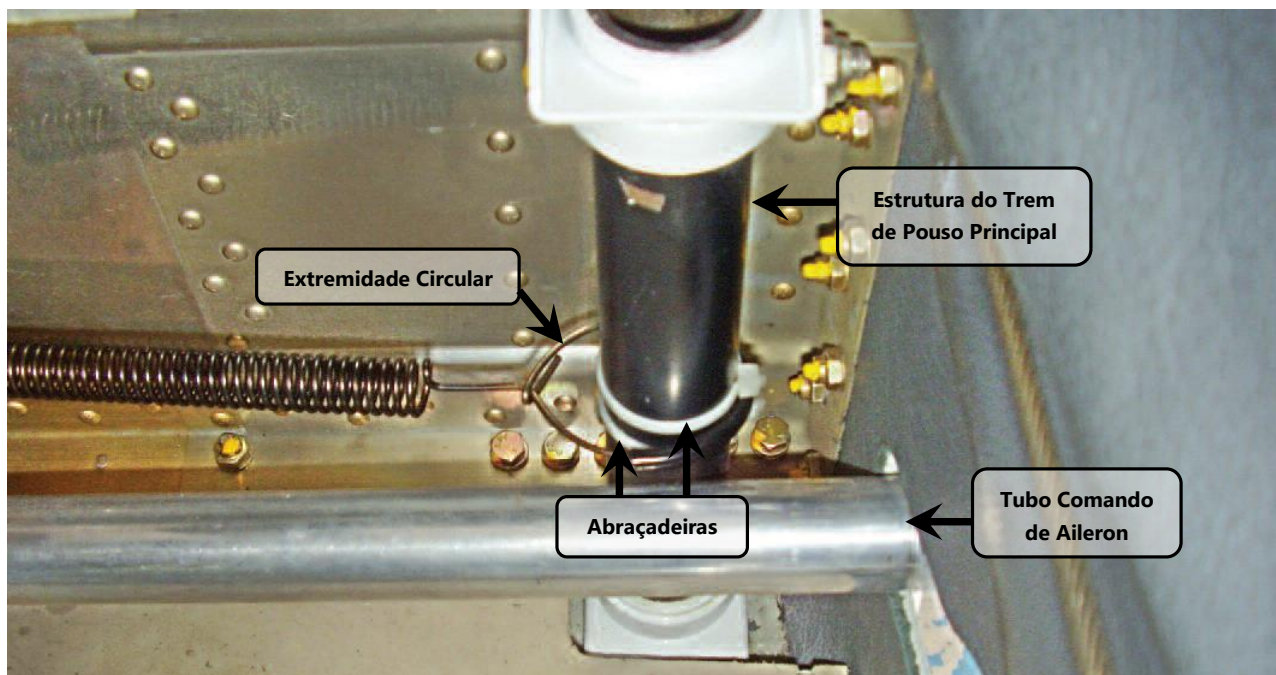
Instalação da mola entre as abraçadeiras
